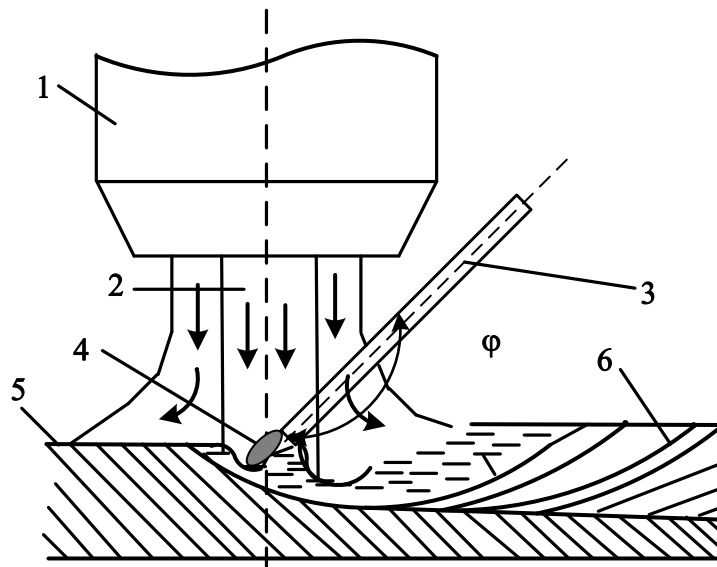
Схема процесса плазменной сварки при замыкании торца присадочной проволоки на сварочную ванну: 1 - плазмотрон; 2 - дуга; 3 - проволока; 4 - активное пятно; 5 - изделие; 6 - шов
